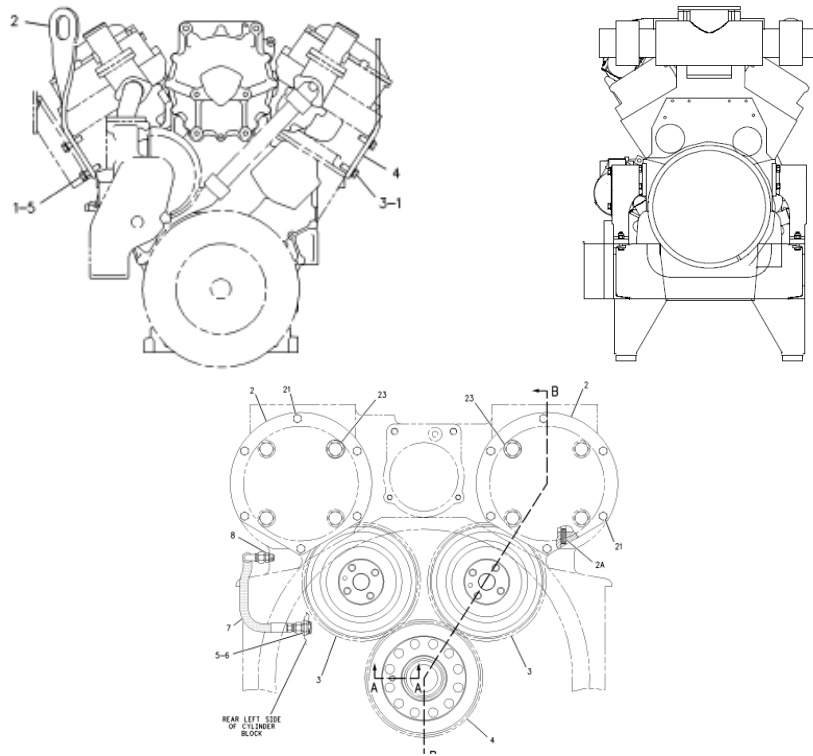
Izda: Distribución del motor (parte delantera) - Dcha: Volante del motor (parte trasera)
